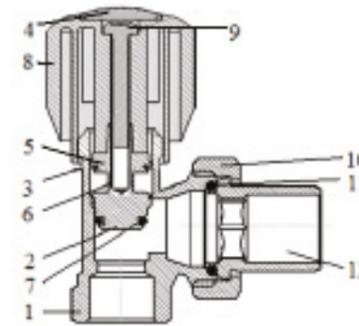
Устройство клапана ручного терморегулирующего (устройство углового и прямого клапанов идентичны)
